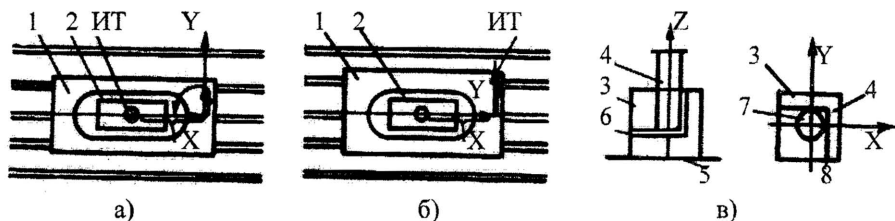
Схемы установки приспособления и заготовки в исходные точки (ИТ)
